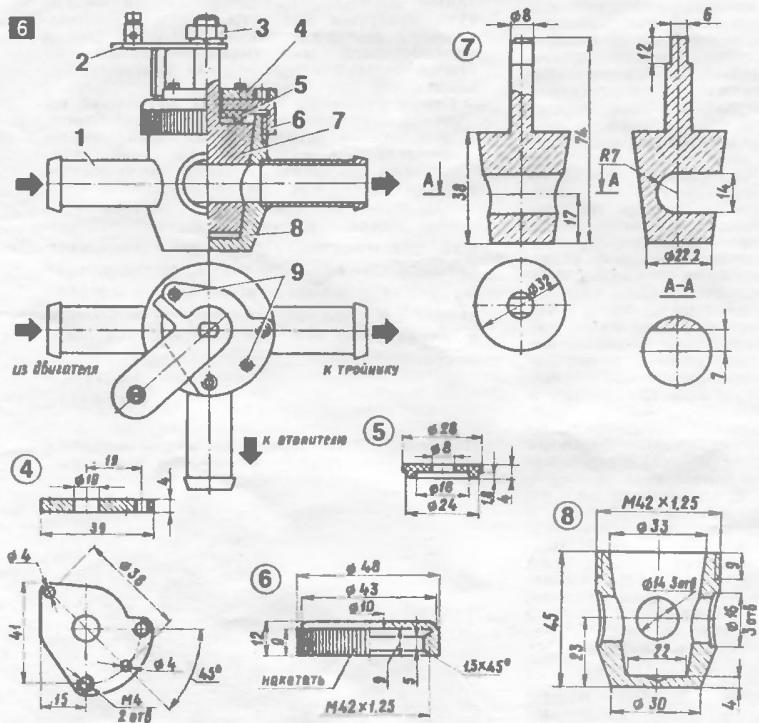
Трехходовой кран: 1 — штуцер (3 шт., размеры как на рис. 7); 2 — рычаг; 3 — гайка и шайба крепления рычага; 4 — пластина; 5 — прокладка (материал — капролон, полистилен, фторопласт); 6 — крышка (материал — нержавеющий металл); 7 — золотник (материал — латунь, бронза); 8 — корпус (материал — латунь, бронза); 9 — винты M4 крепления крышки (отверстия для них сверлить в крыше после сборки). Рабочие поверхности золотника и корпуса взаимно притереть.
